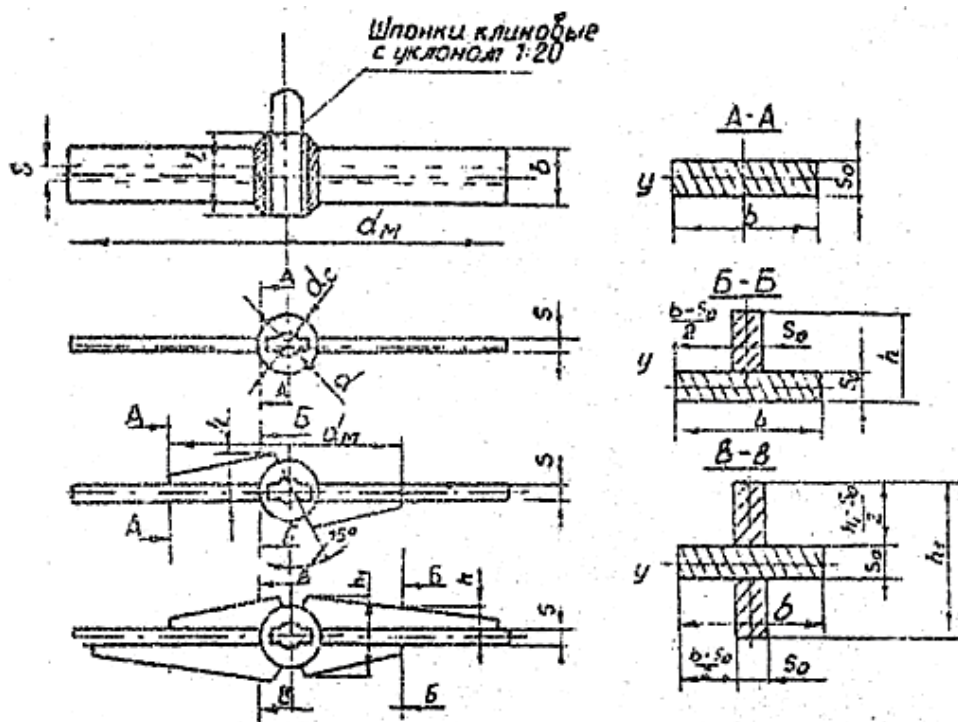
Основные типы сварных лопастных перемешивающих устройств:
